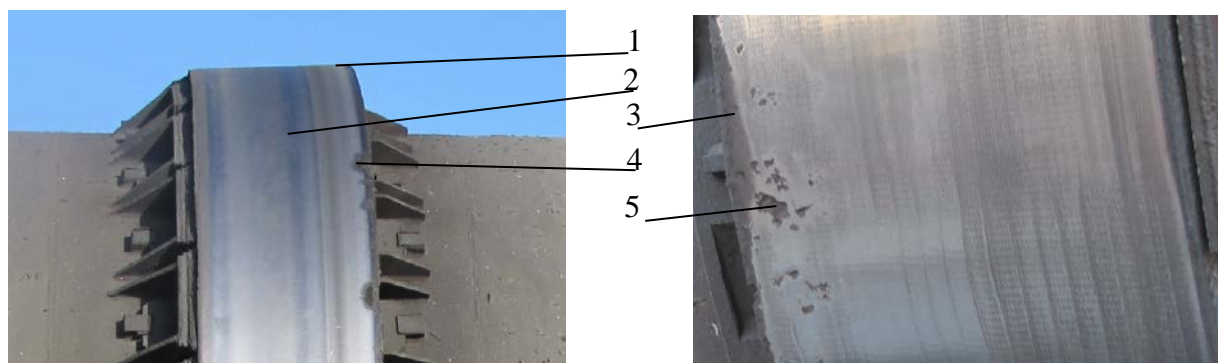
Повреждения бандажей типа П вращающейся печи 5×185 м: 1- конусность; 2 - следы неравномерного износа; 3, 4 - кромочные изломы; 5 - очаг выкрашивания
